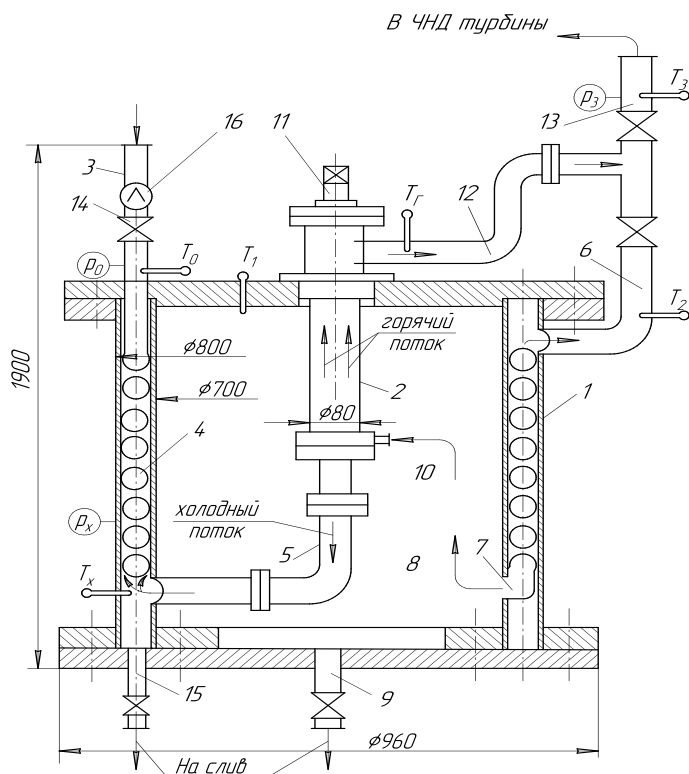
Конструктивная схема воздухоосушителя системы защиты паровой турбины от стояночной коррозии
